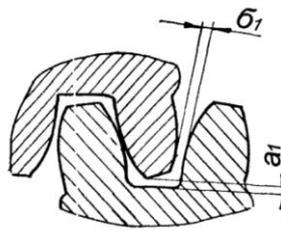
Продольный разрез цилиндрической зубчатой пары валоповоротного устройства турбины К-300-240 ХГТЗ [4]
